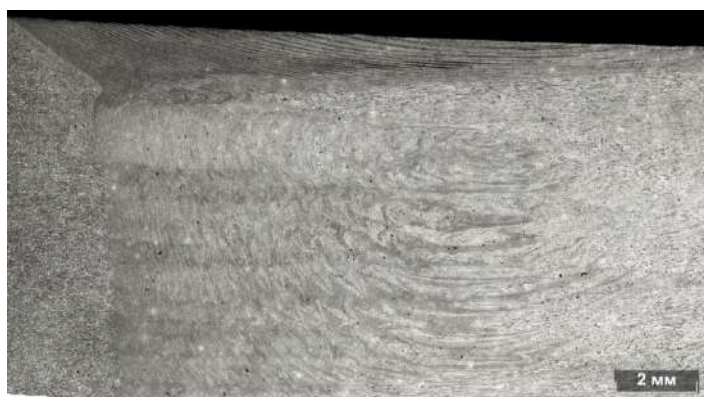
Внешний вид сварного соединения (режим 8)
